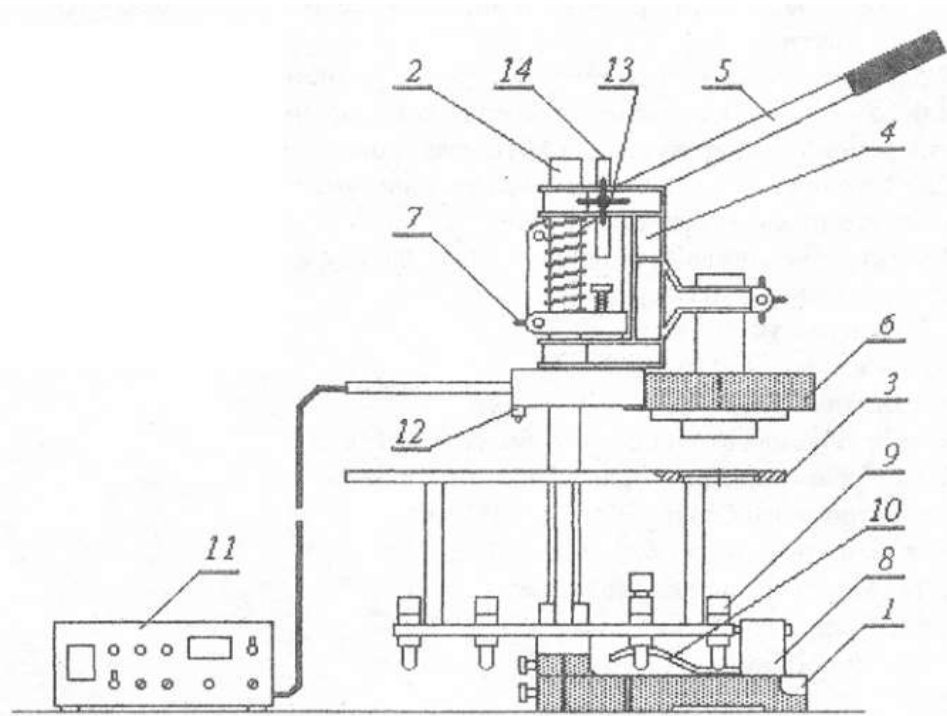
Установка заварки стаканчиків кришками УСС-2:
